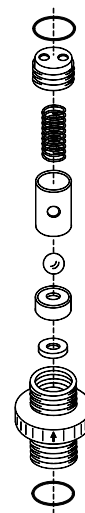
Клапан исполнения DN 4 из нержавеющей стали, подпружиненный
